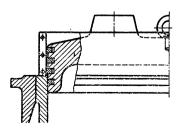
Приспособление для ввода колец в цилиндр, изготовленное из листовой стали толщиной 1,5 мм
